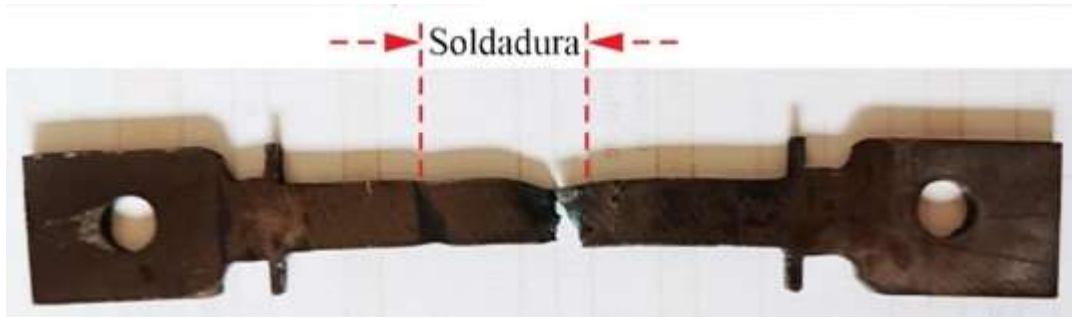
Tratamiento térmico post soldadura de 8 h a 730°C
